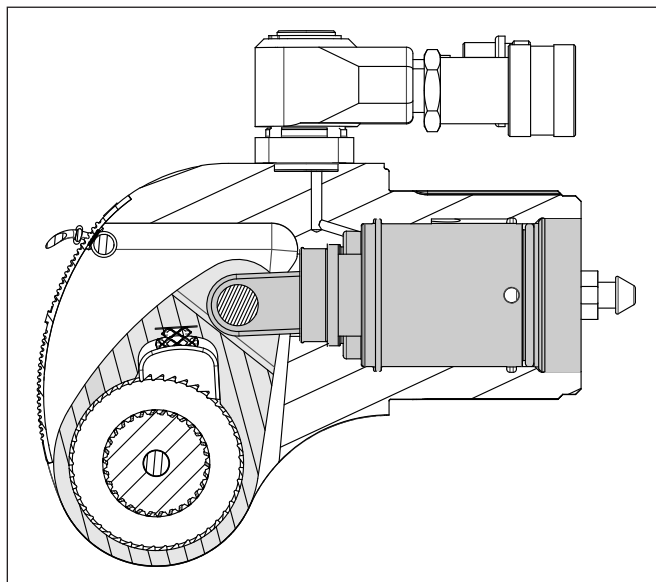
Вид в разрезе, установка в рабочее положение цилиндра и рычага
